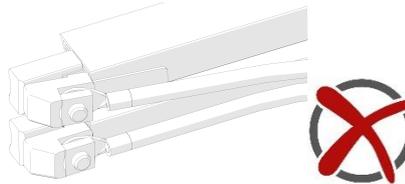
Falsch: Klemmflügel steht über dem Isolierprofil ab
